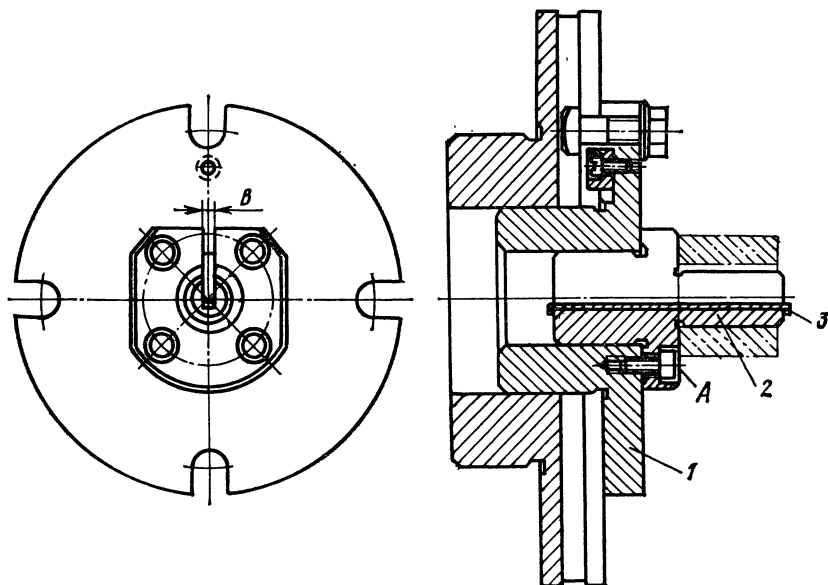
Приспособление для протягивания шпоночного паза во втулках и зубчатых колесах
